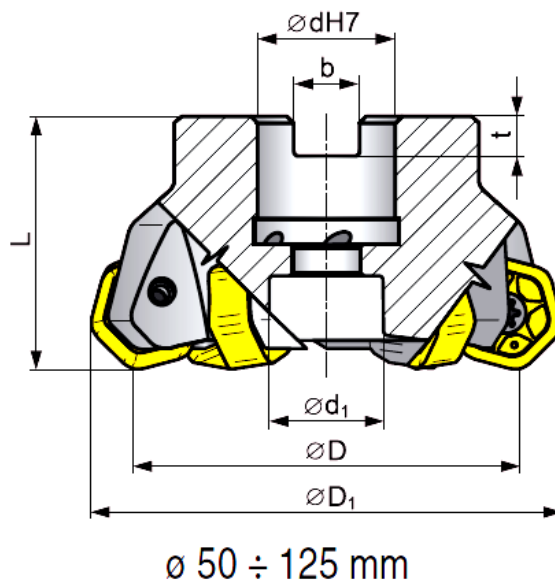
Čelní fréza Pramet Tools, s.r.o. typ 63A06R-S45HN09C-C
